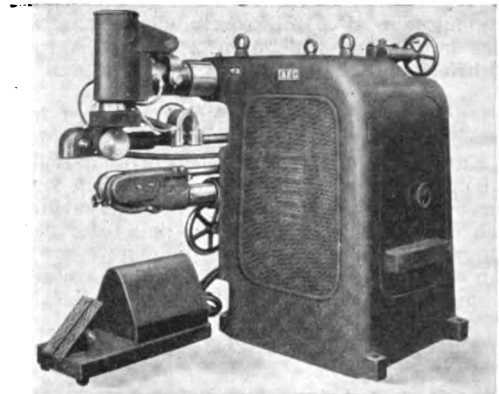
Punkt- und Rollennaht-Schweißmaschine.
